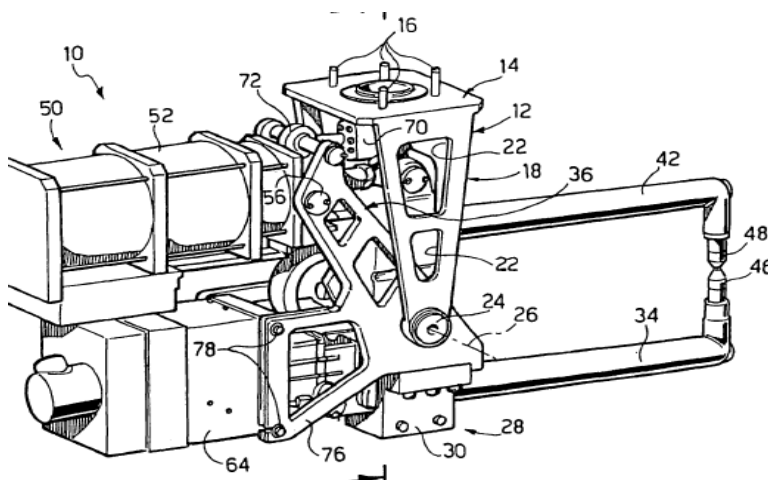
Componentes pinza de soldadura por puntos (Porta, 2008)
